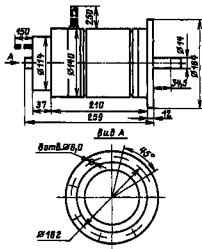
Габаритные и установочные размеры двигателя АСД-2
